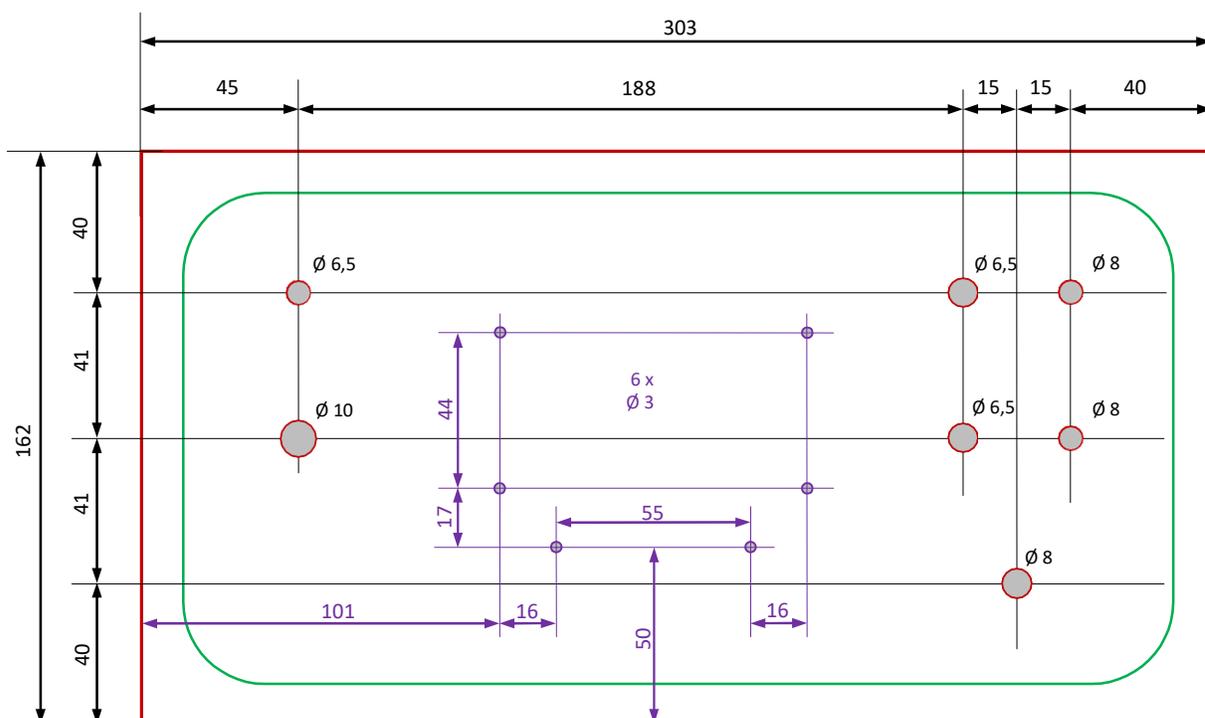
plan de l'usinage de la face avant – Échelle ½
